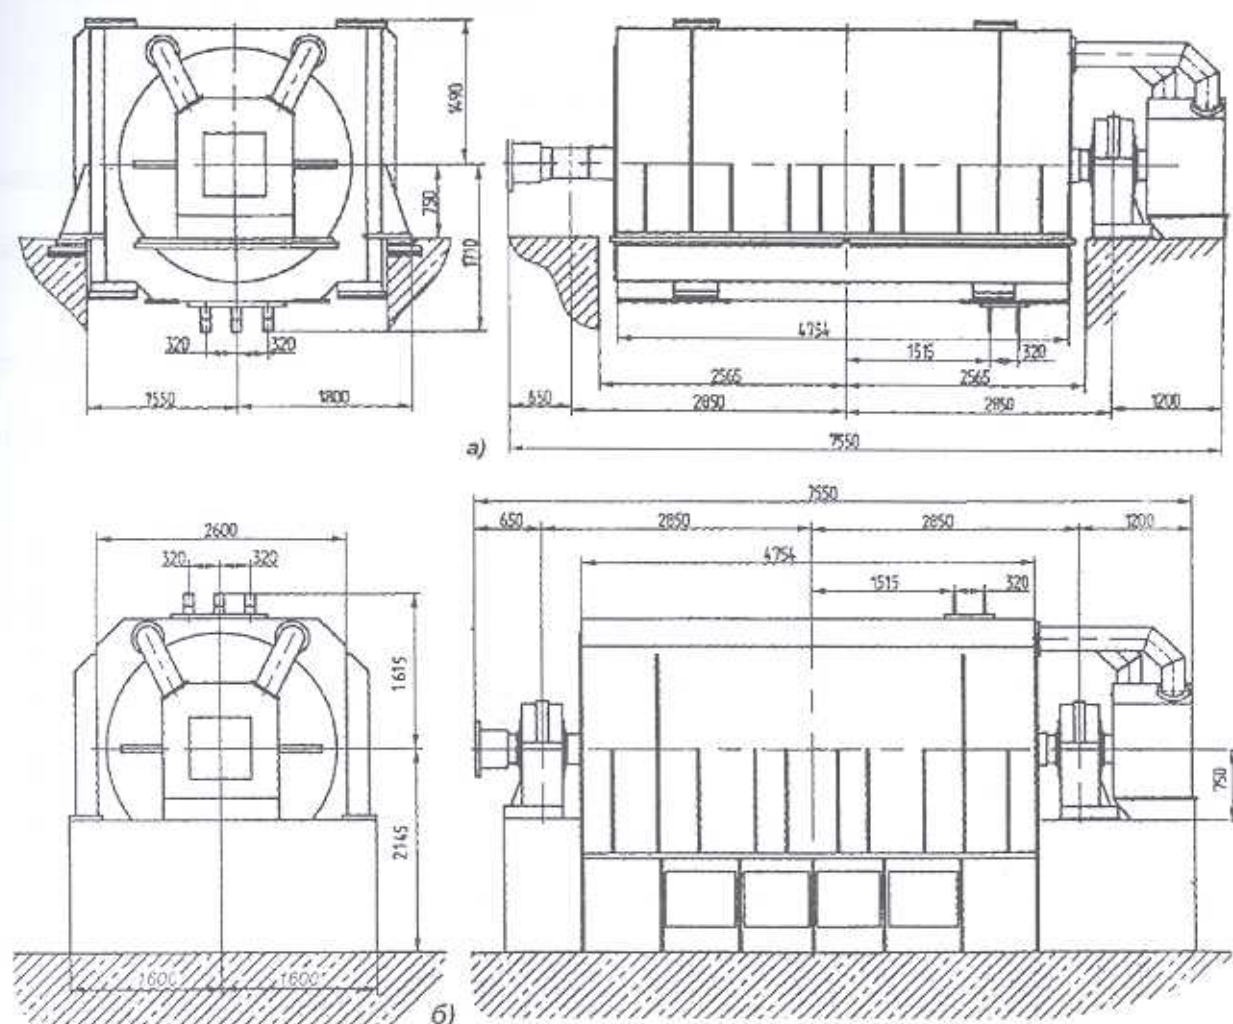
Установочный эскиз с габаритными размерами турбогенератора типа ТФ-32-2 (БСВ):
